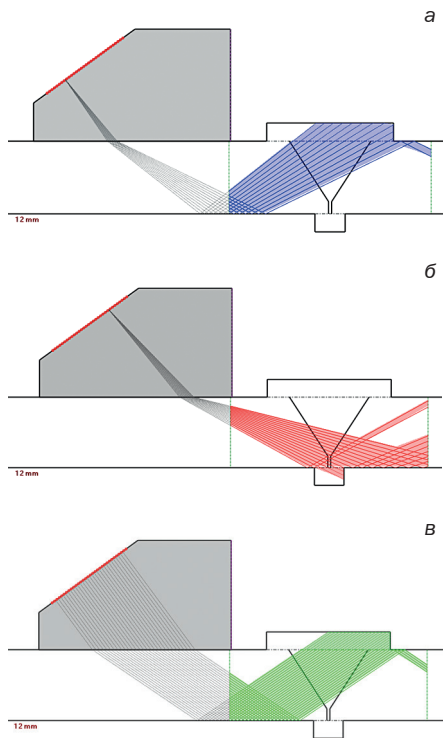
Пример мульти-группного плана прозвучивания поперечного сечения сварного шва: видно, что для его реализации требуется ФР-преобразователь и преломляющая призма достаточно больших размеров
